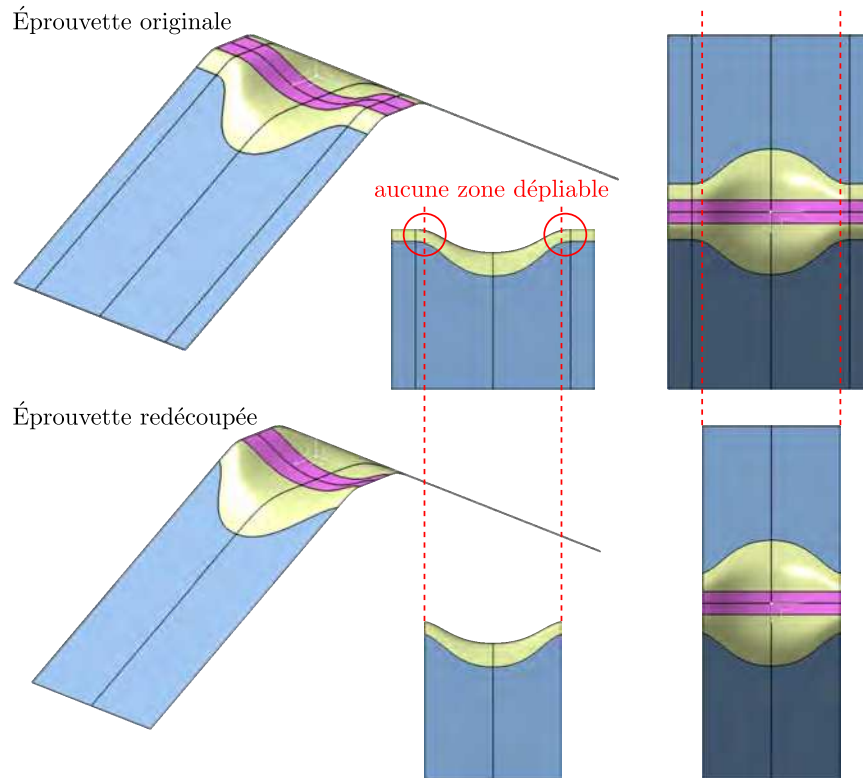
Schéma de principe du découpage de l'éprouvette M10R5SC1
